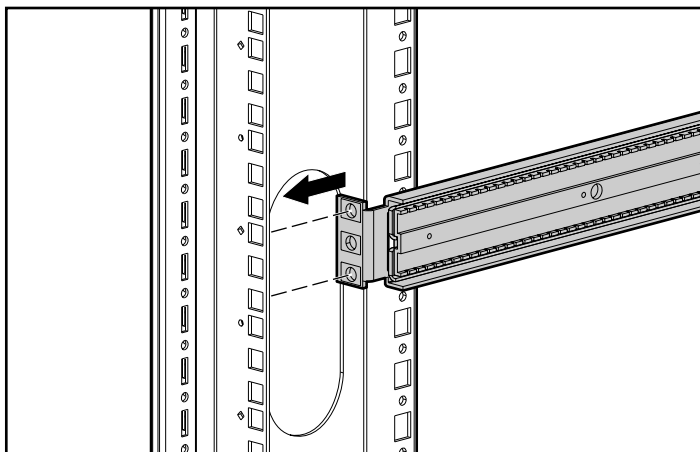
Alignement de la face avant du rail externe sur le rack
